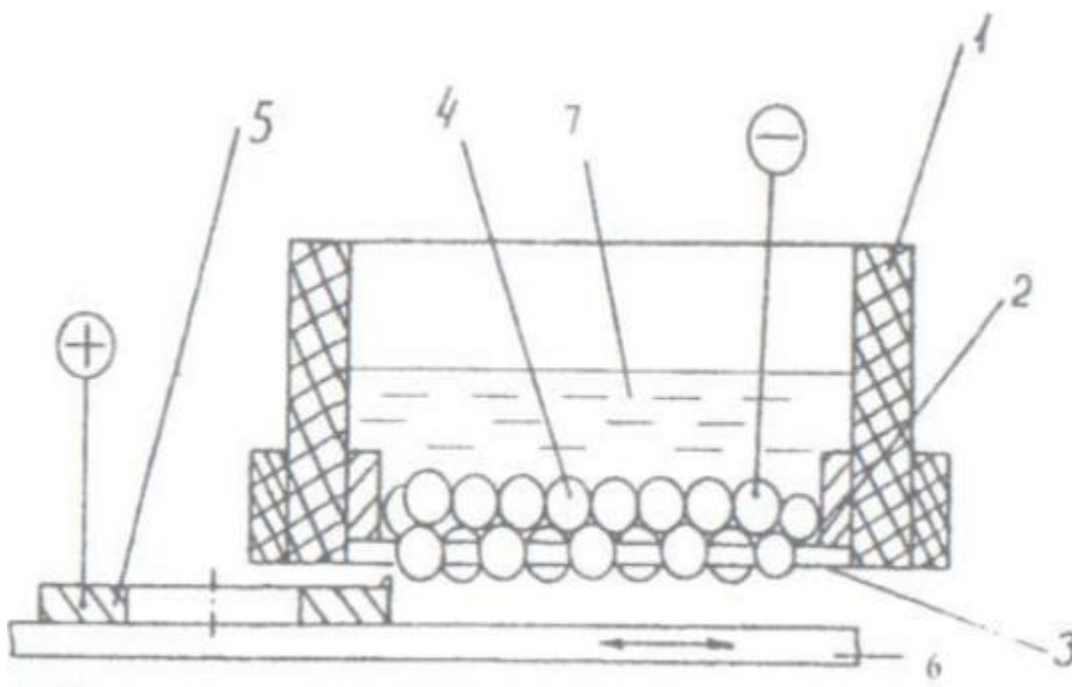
Схема виброударной комбинированной зачистки поверхности гранулами
